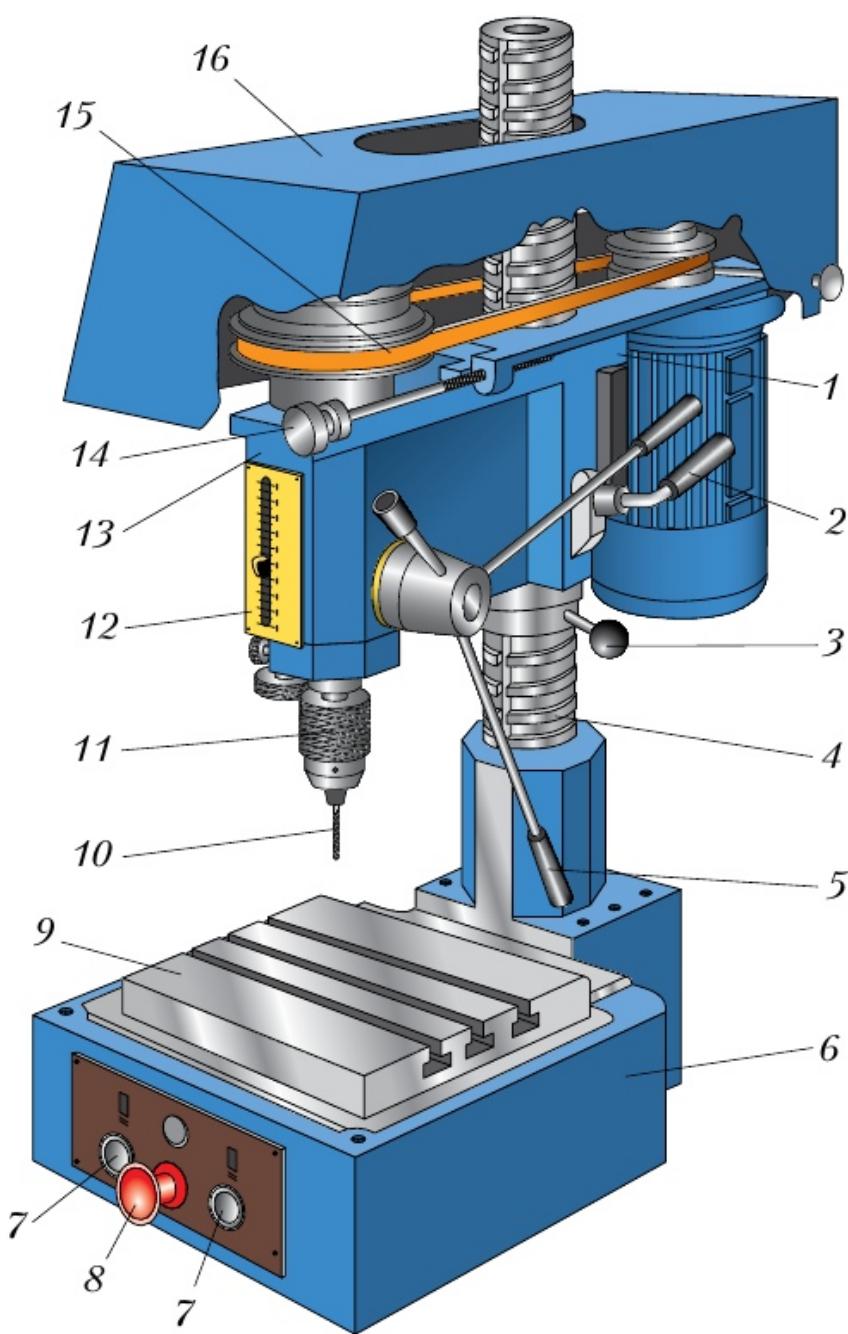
Устройство сверлильного станка: 1 – шпиндельная бабка с электродвигателем; 2 – ручка фиксирования шпиндельной бабки; 3 – рукоятка подъёма и опускания шпиндельной бабки; 4 – винтовая колонна; 5 – рукоятка подачи шпинделля с патроном; 6 – станина; 7 – кнопка включения; 8 – кнопка выключения; 9 – стол; 10 – сверло; 11 – патрон; 12 – шкала установки глубины сверления; 13 – шпиндельная коробка; 14 – винт натяжения ремённой передачи; 15 – ремённая передача; 16 – кожух ремённой передачи
